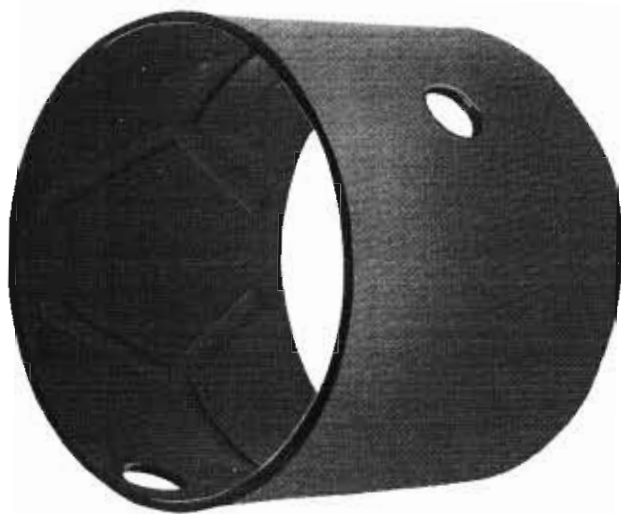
Soldadura de prevención en un bastidor estandar SD
